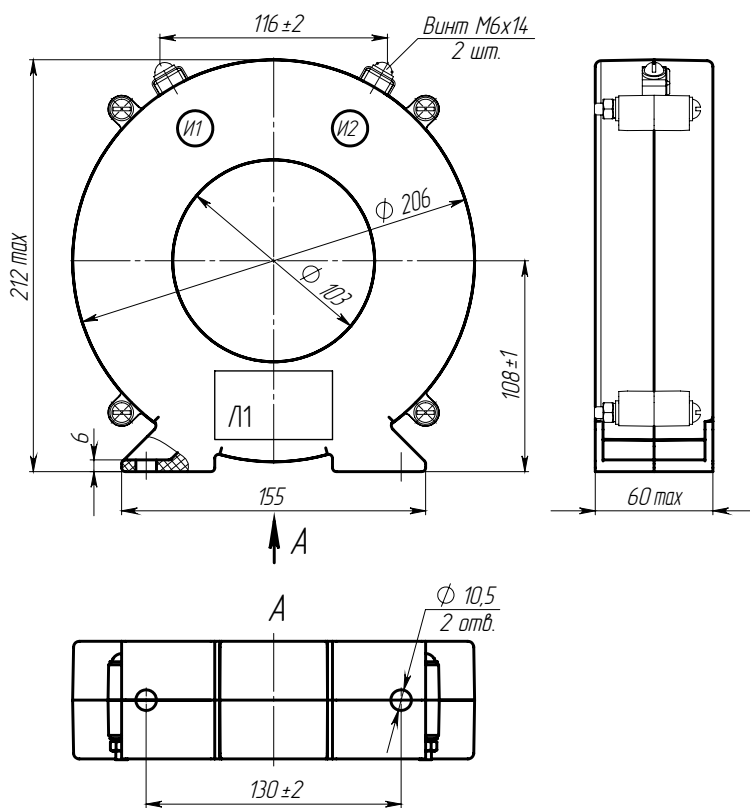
Общий вид трансформатора ТНШЛ-0,66 в пластмассовом корпусе на токи 600–2000 А
